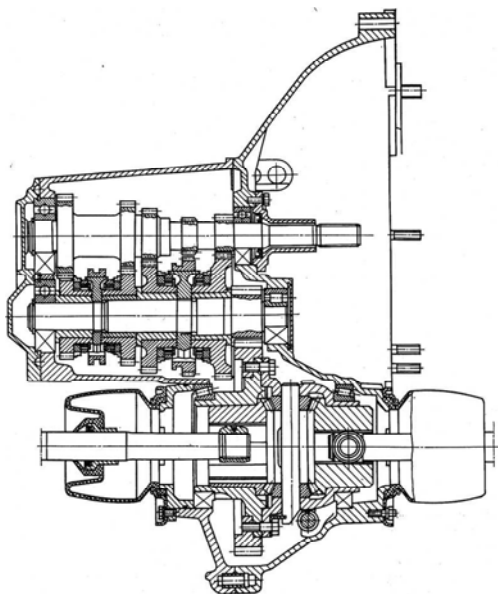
Конструкция двухвальной коробки передач и главной передачи переднеприводного автомобиля с поперечным расположением двигателя
